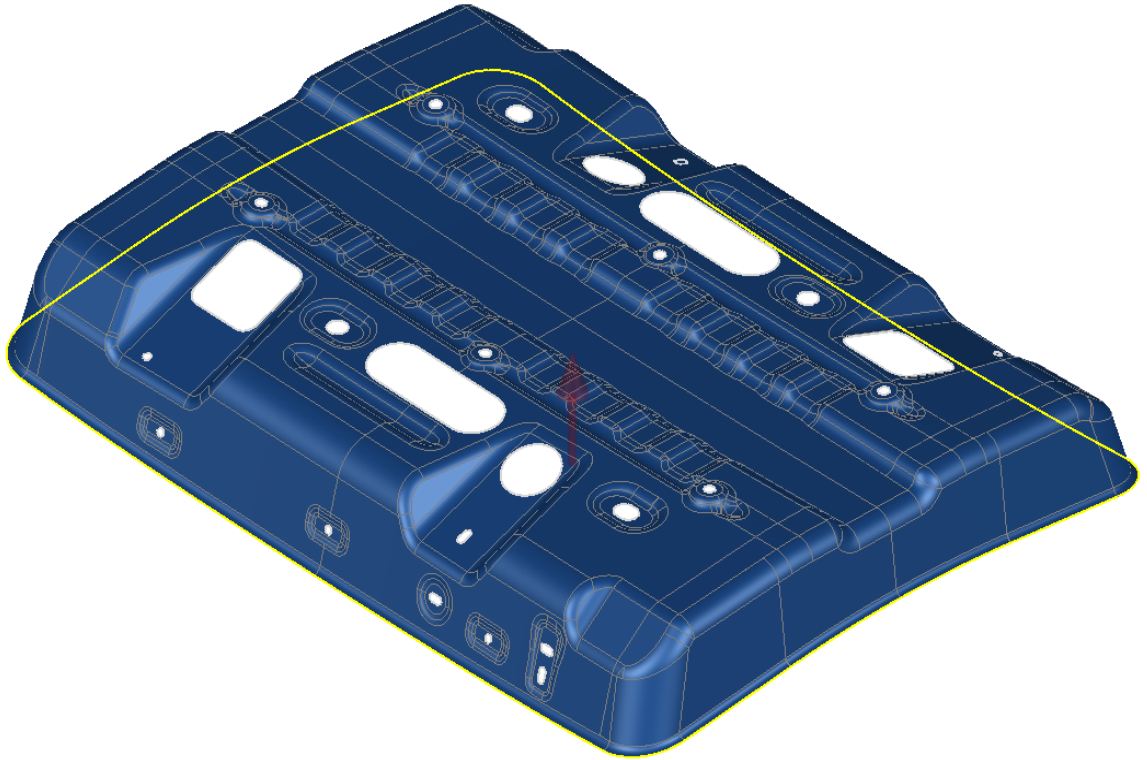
Математическая модель 8450006203_MBR CROSS ROOF RR 1st 160406
